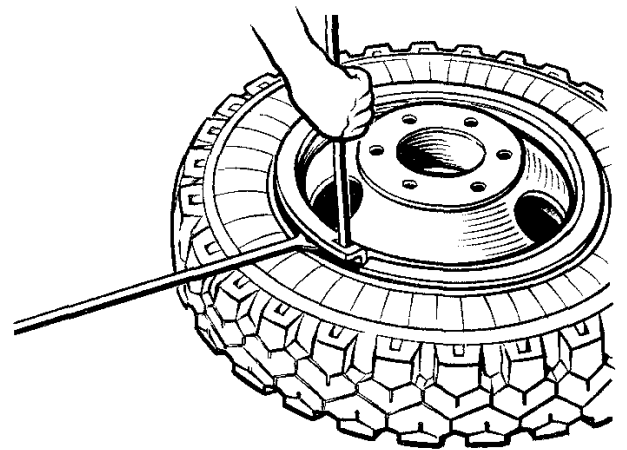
Установка прямой лопатки в прорезь бортового кольца
